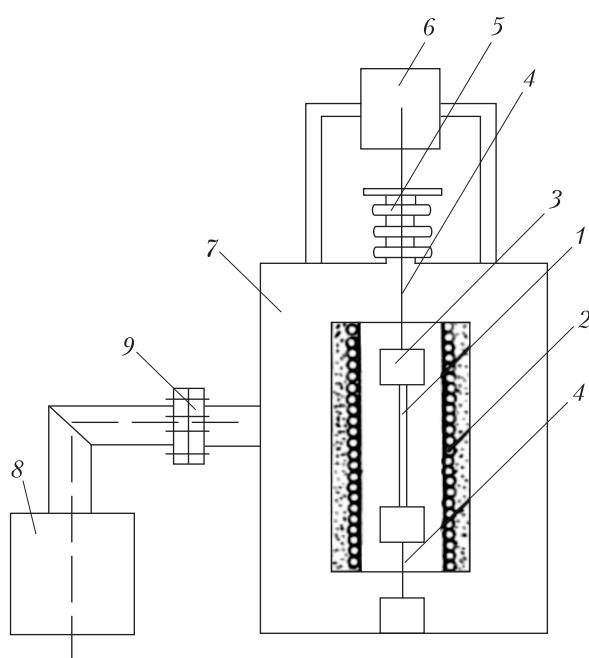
Схема установки для термообробки и выравнивания прутков из гафния: 1 – пруток из гафния, 2 – печь сопротивления, 3 – концевые захваты, 4 – тяги, 5 – сильфон, 6 – устройство для создания нагрузки, 7 – вакуумная камера, 8 – откачное устройство, 9 – клапан
